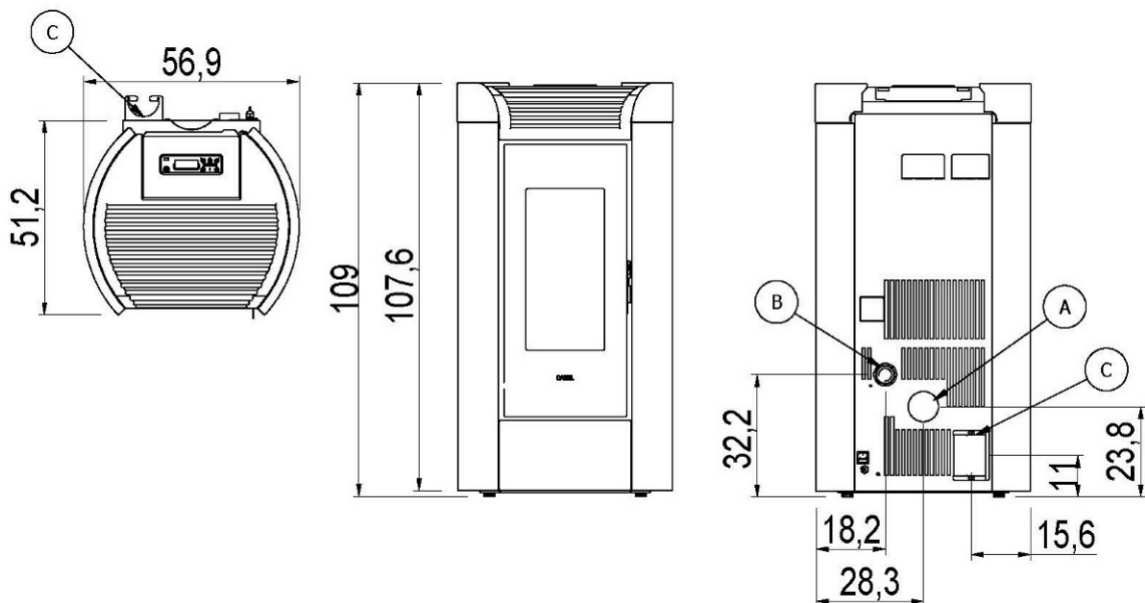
Dimensions générales: Prince 11 - Prince Plus 11
